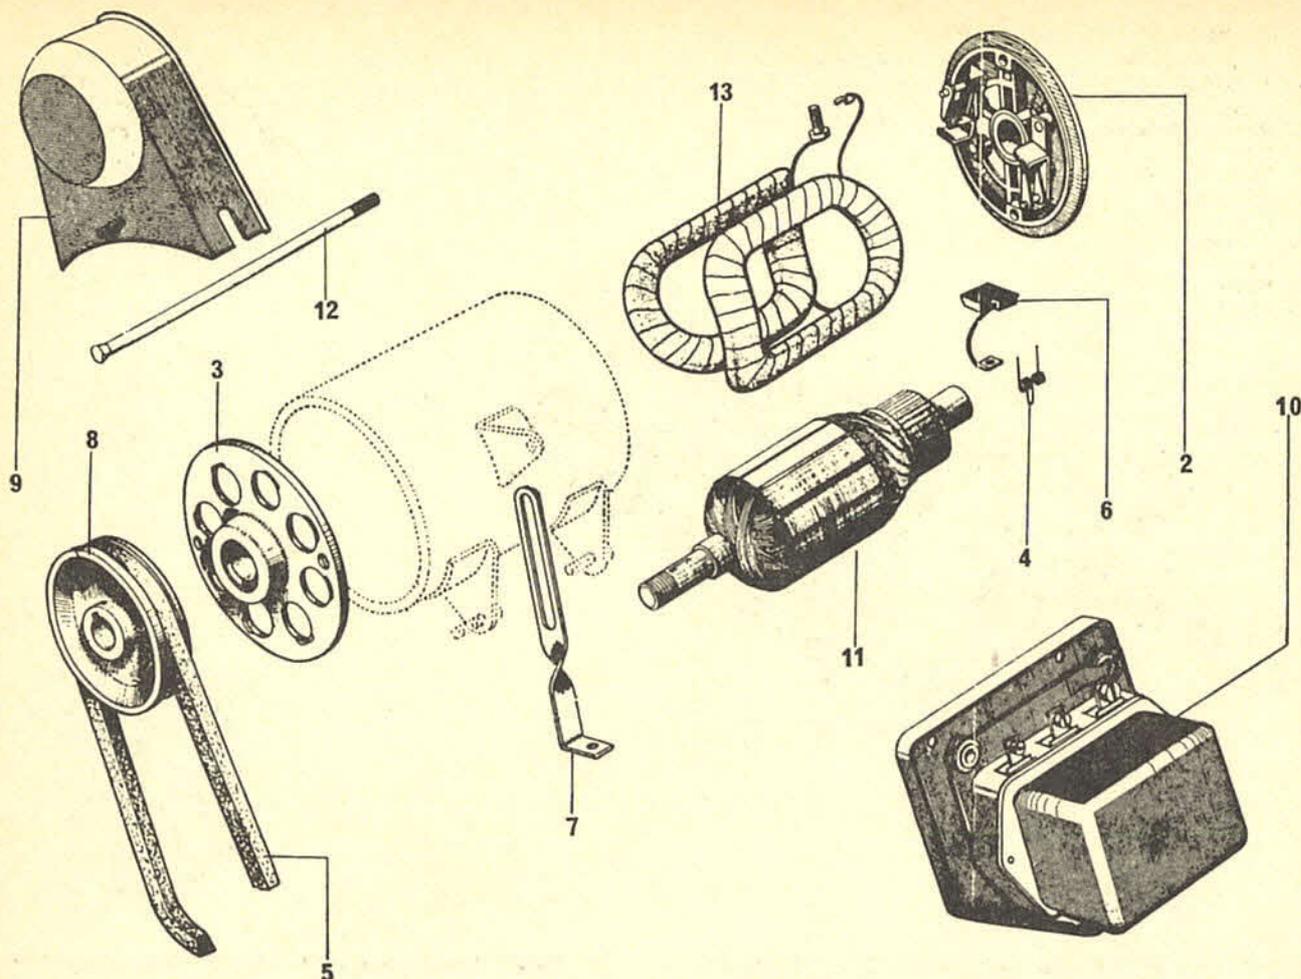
Montagebild der zerlegten Lichtmaschine 12 V
